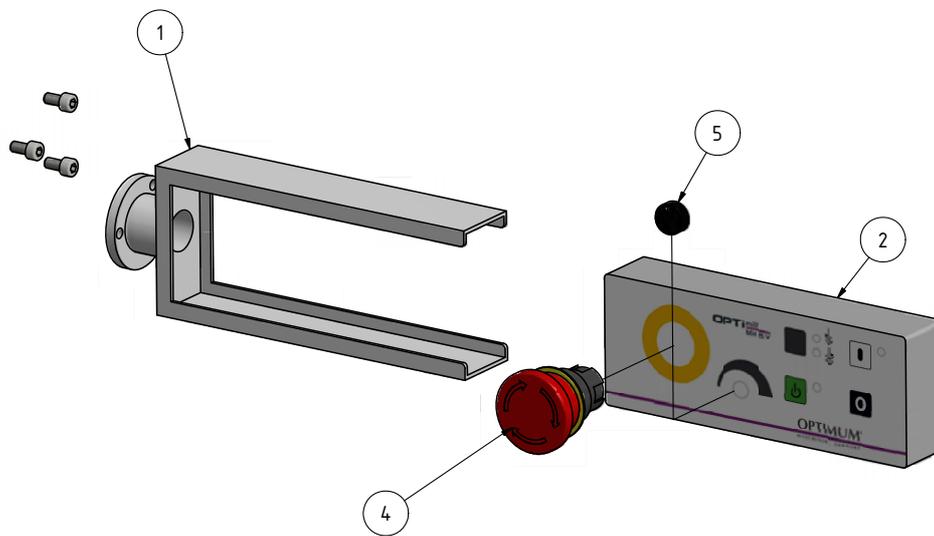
Fräsfutterschutz - Milling chuck cover
